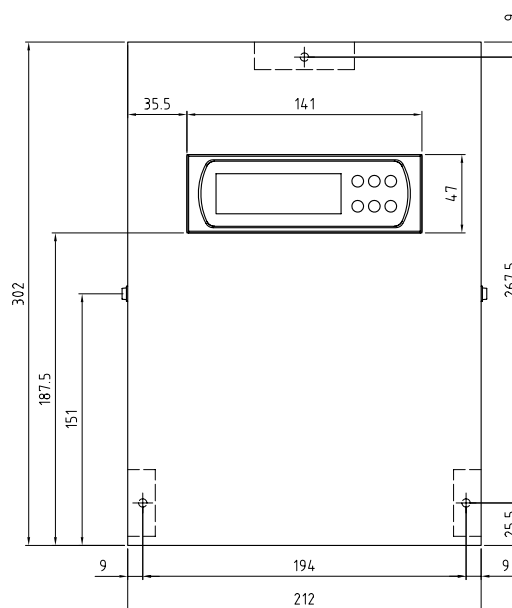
Dimensions du régulateur de pompe à chaleur chauffage, version murale
